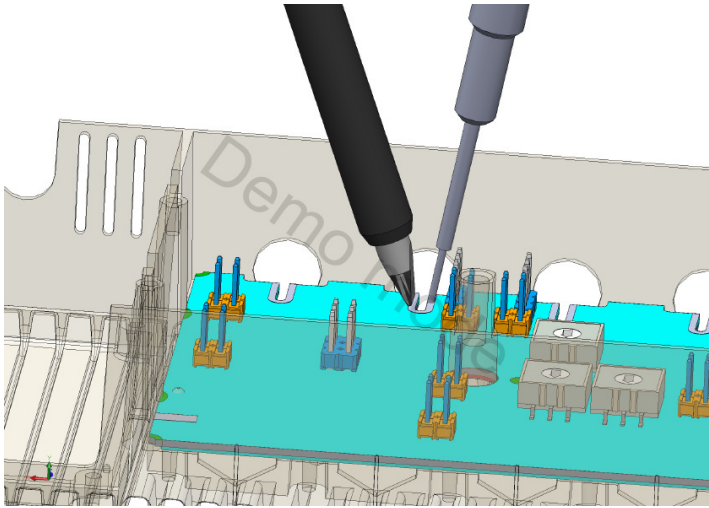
Lötcolben Pad-Pin-Layoutvorschlag
